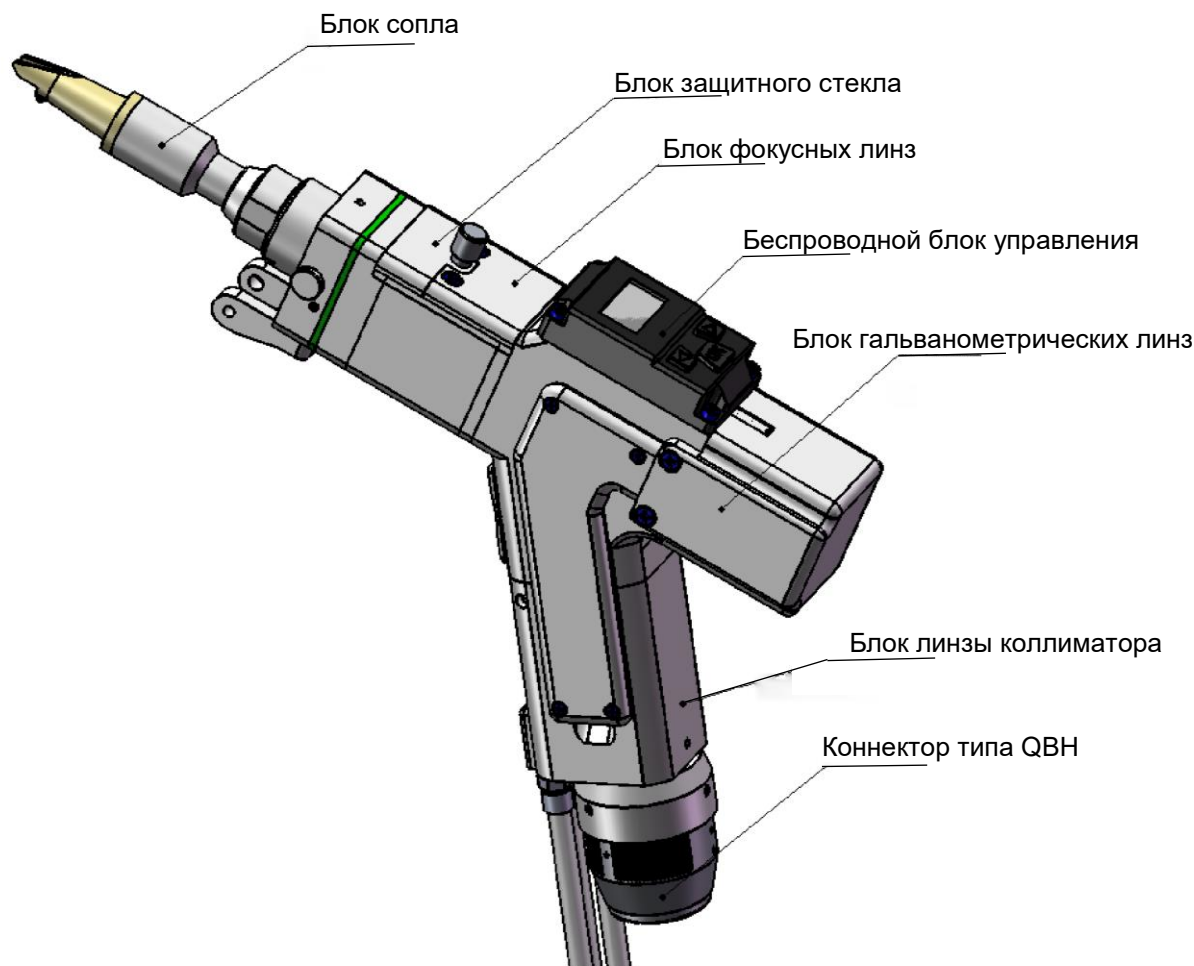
Схема общего вида пистолета лазерной сварки HW970
